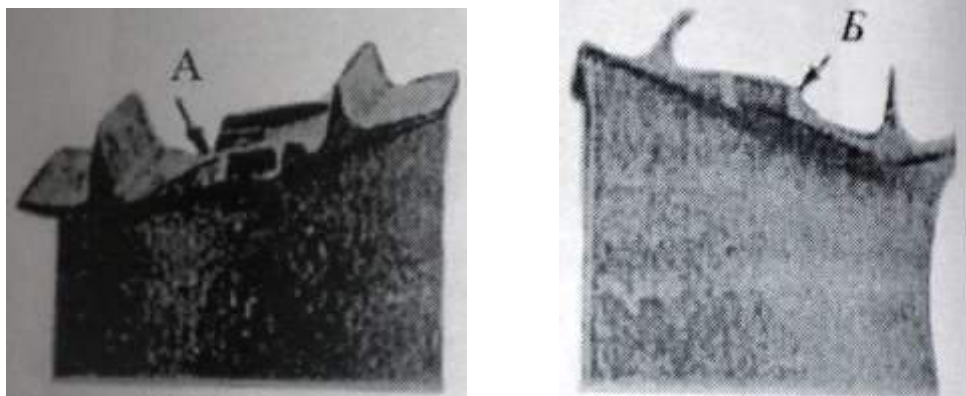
Бічний ризик для контактної та неробочої поверхні полки
